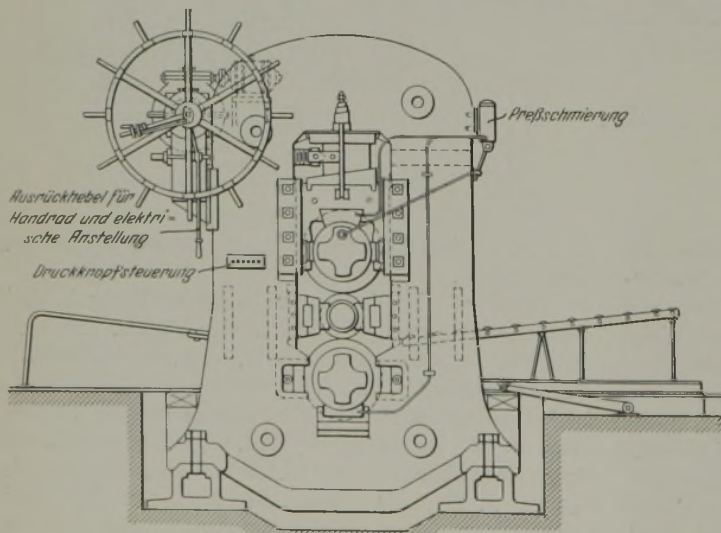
Walzgerüst mit Keilanstellung sowie mit Handrad- und elektrischer Anstellung (Bauart Klein, Dahlbruch).
